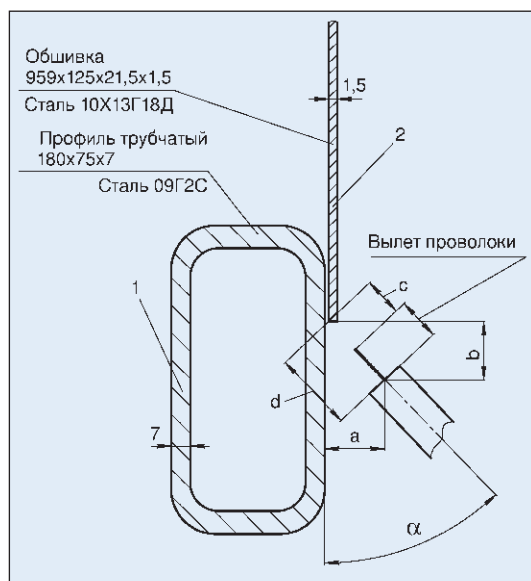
Схема сварки горизонтального шва на вертикальной плоскости
